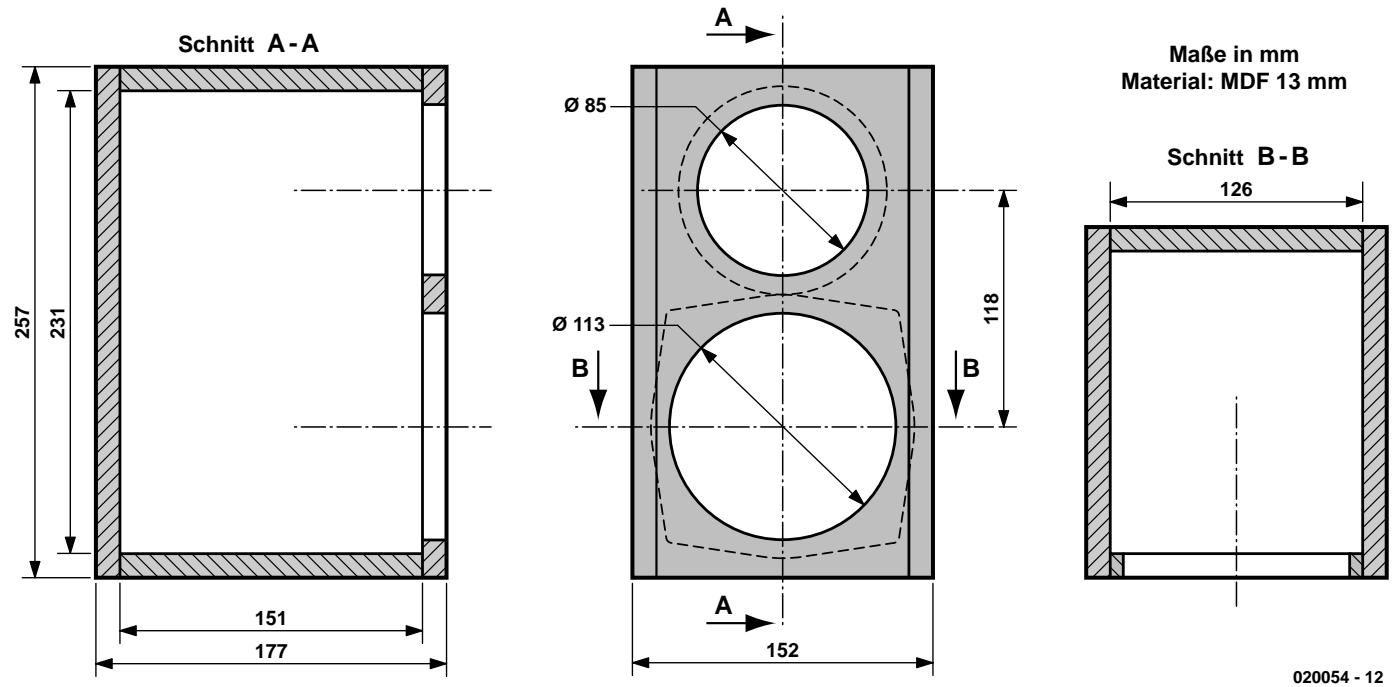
Komplett bemaßte Bauzeichnung der Box in 13 mm starkem MDF.
